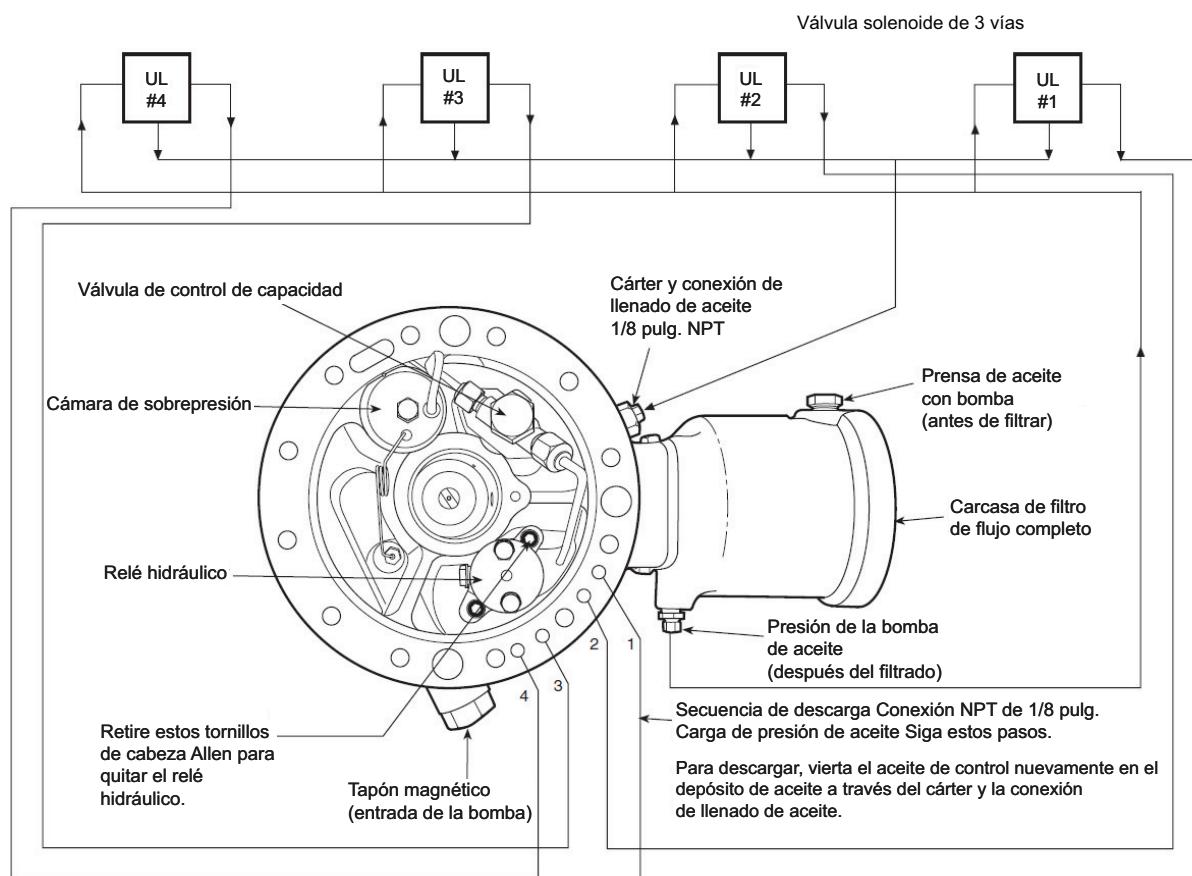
Conjunto de cabezal de cojinete 5H 120/126
